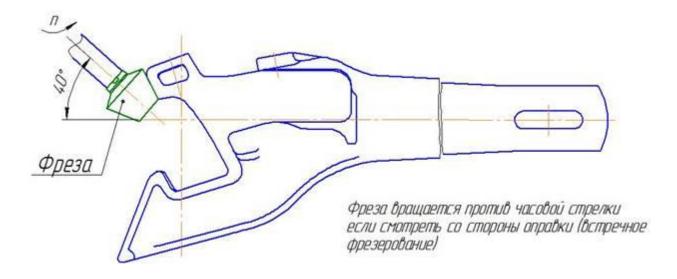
Схема фрезерования ударной поверхности малого зуба
